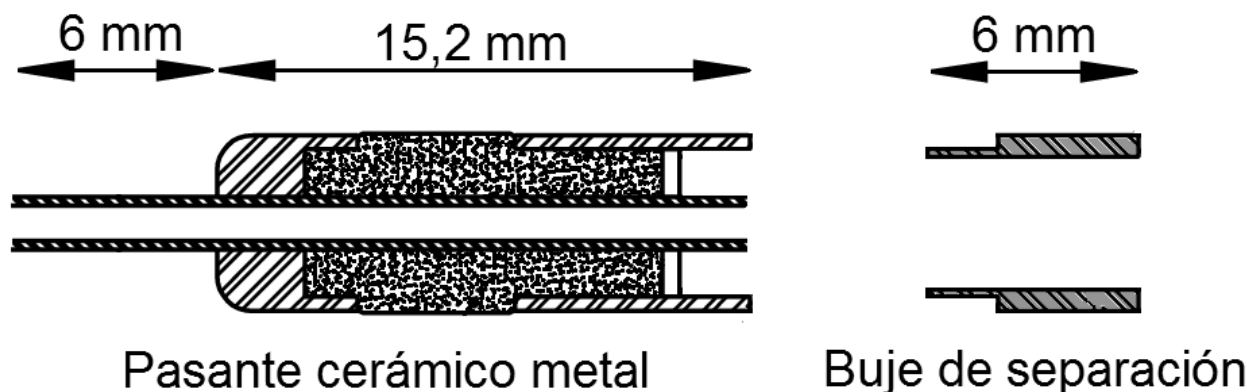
Dimensiones del pasante y el buje a soldar con láser
